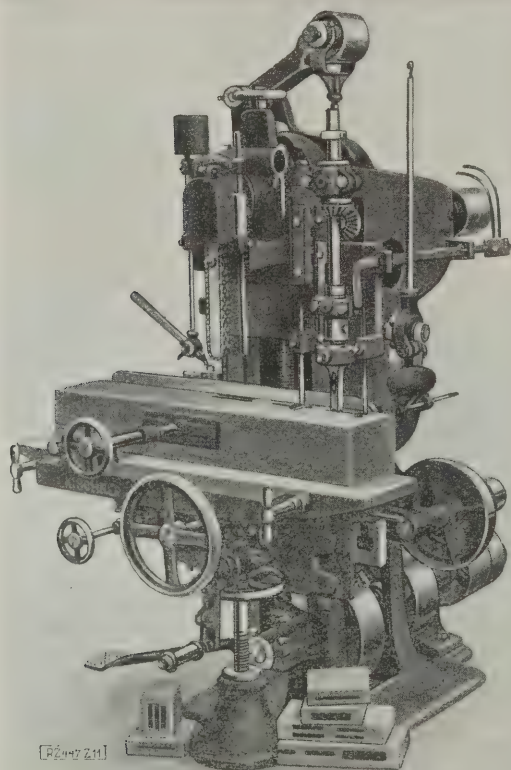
Zapfenloch-Kettenfräsmaschine.
